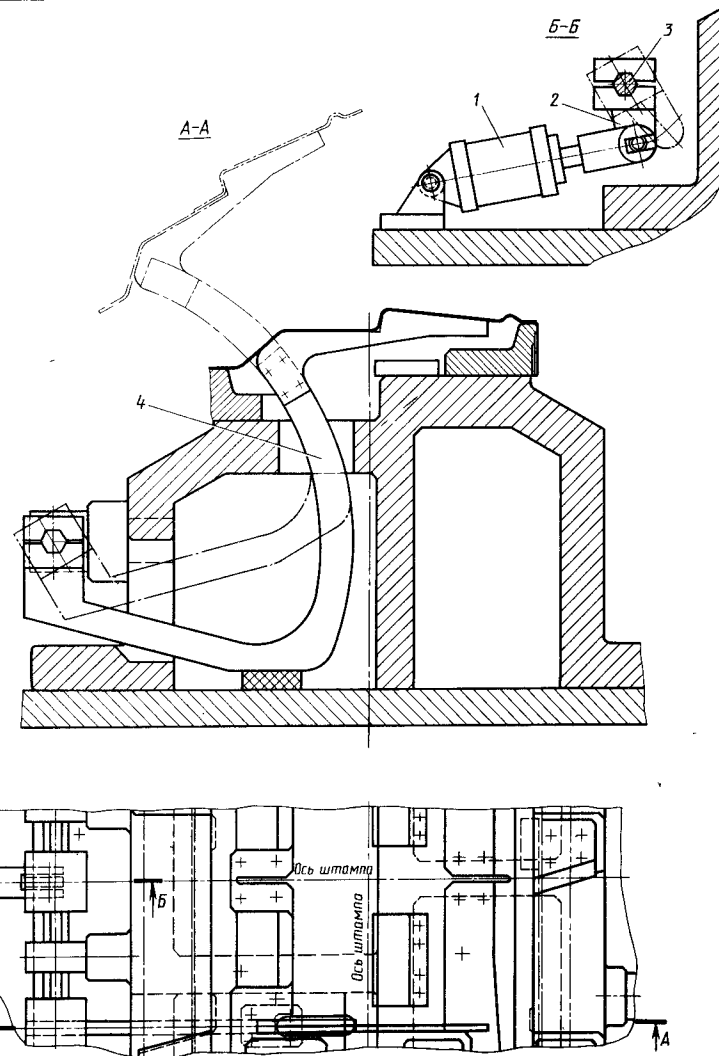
Примеры средств механизации для подъема заготовки (детали) в штампе
